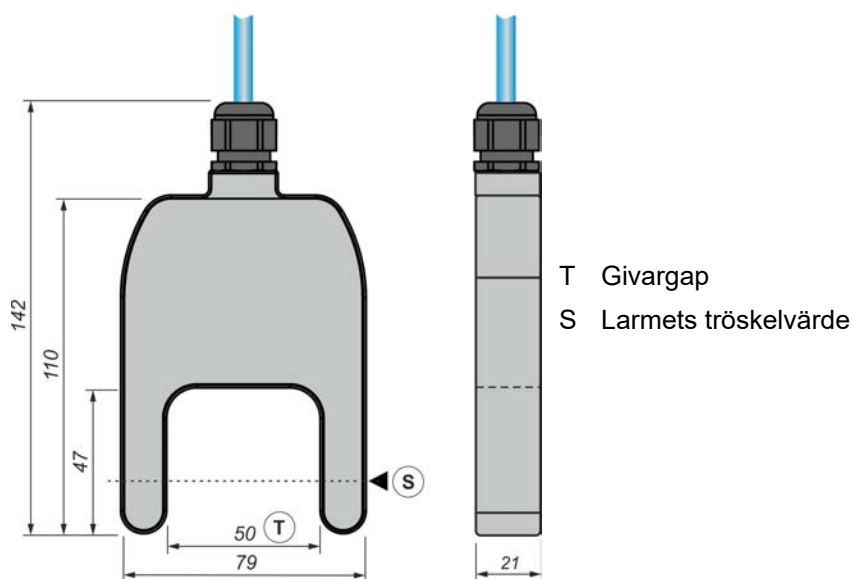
Slamgivare idOil-SLU – struktur och mått (mm)
